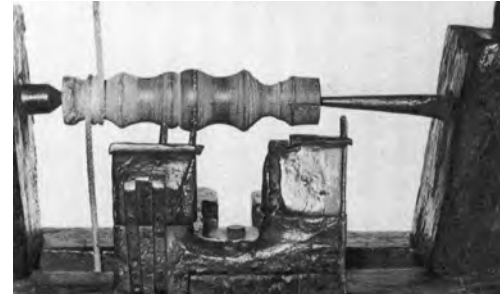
Hand-Werkzeug-Technik: Wippendrehbank vor 1800, über eine Schnur mit Fusspedal angetrieben (Benad-Wagenhoff et. al. 1993, S. 190)
